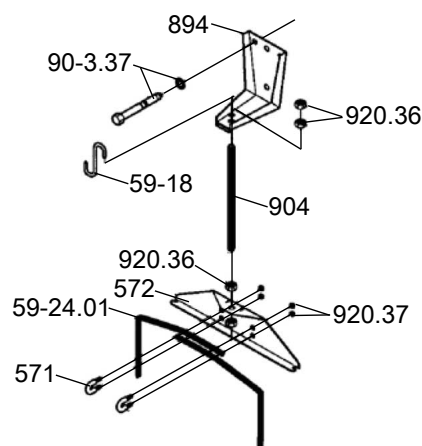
Исполнение консоли для типоразмеров 200-402, 200-403, а также типоразмеров с номинальным диаметром напорного патрубка DN 100 и DN 150
